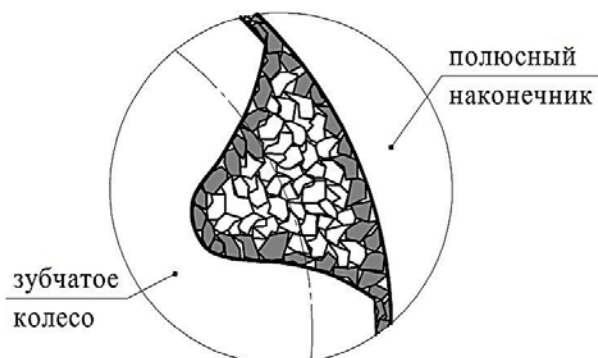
Схема расположения уплотненного абразивного бруска во впадине зубчатого колеса [12]
